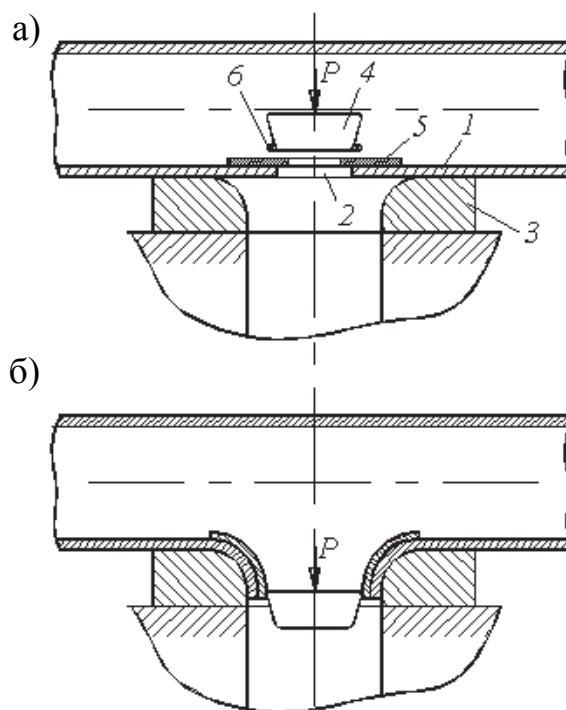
Способ отбортовки фланца в стенке трубы:
